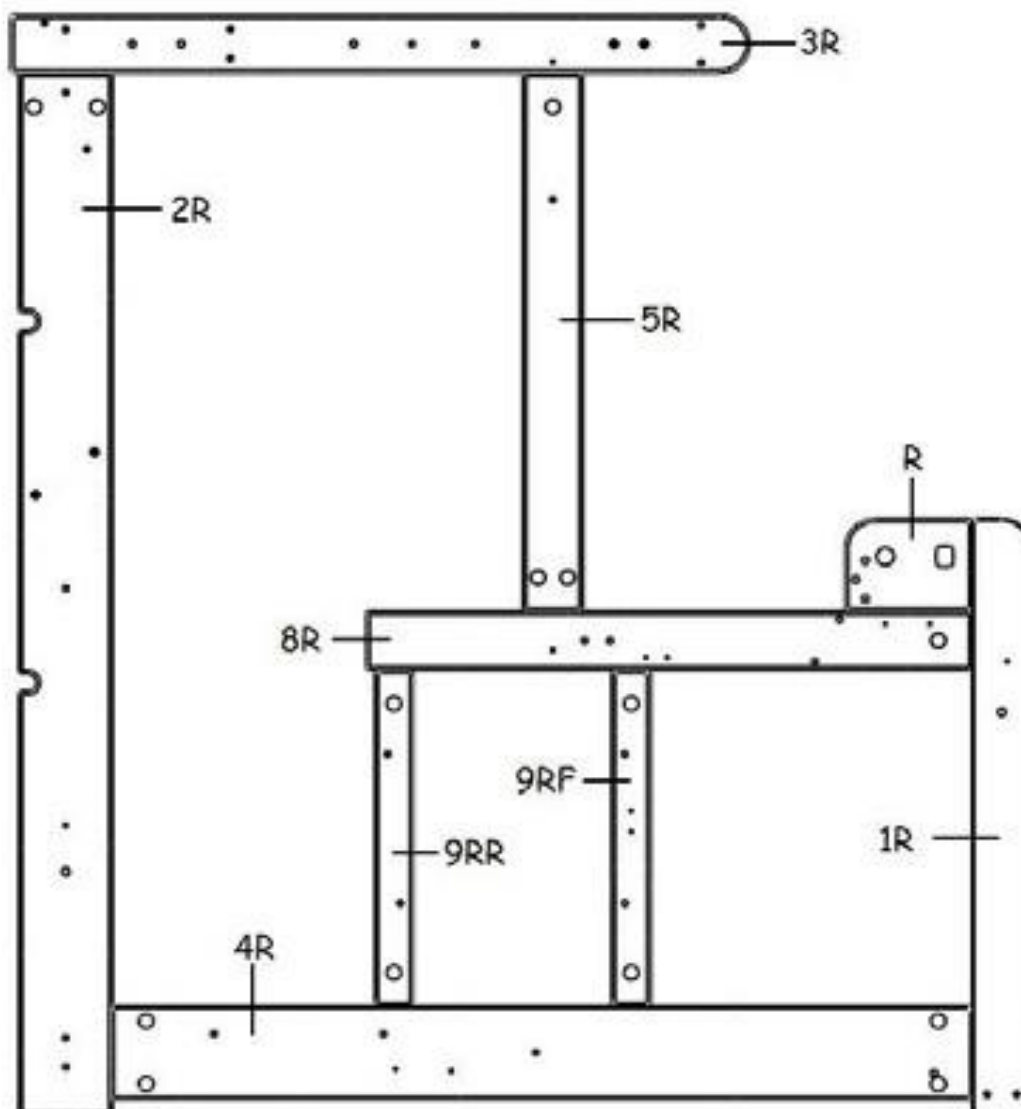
Baugruppe des rechten Seitenrahmens, Innenansicht
